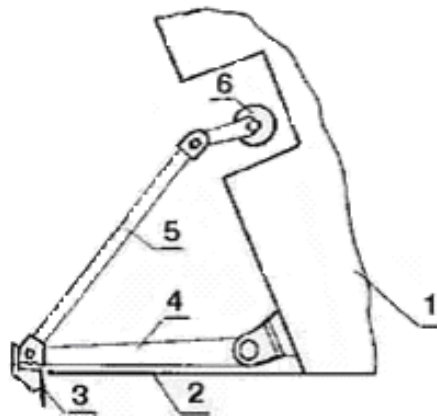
Схема приводу кормового інтерцептори [10]: 1 - корпус катера; 2 - транцева плита; 3 - інтерцептор; 4 - важіль; 5 - тяга; 6 - привід
